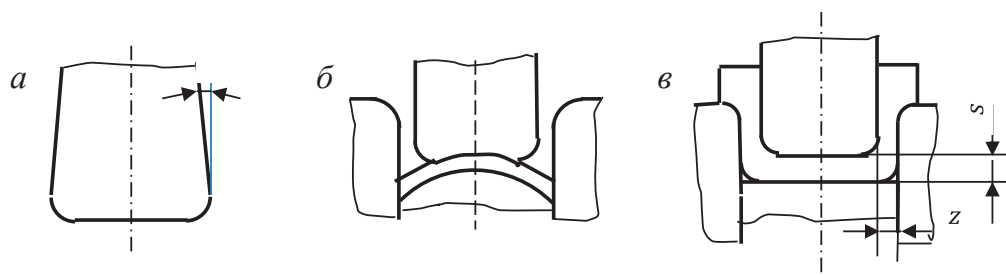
Схемы рабочих частей штампов для гибки скоб:
